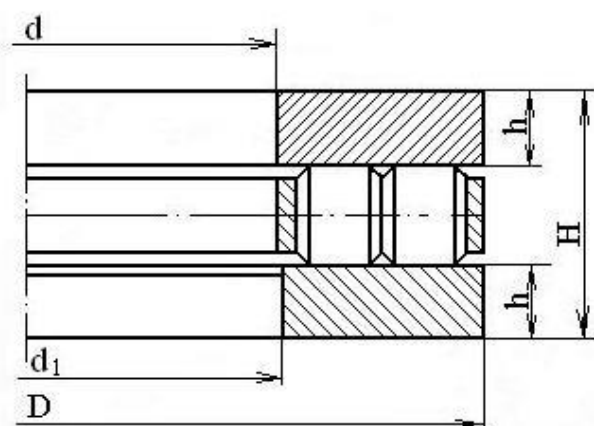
В.12 – Подшипник роликовый упорный двухрядный
